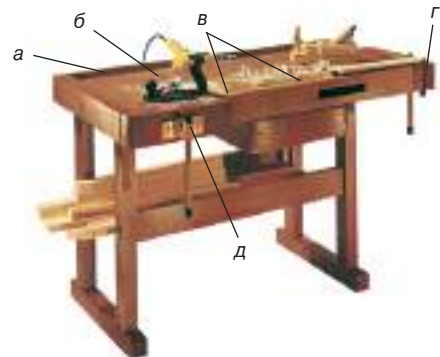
Столярный верстак: а — место для инструментов; б — крышка верстака; в — гнездо для клиньев; г — задняя зажимная коробка; д — передний зажимной винт
